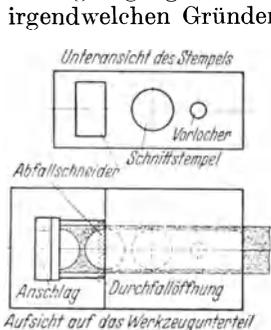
Schnittwerkzeug mit Abfallschneider.
